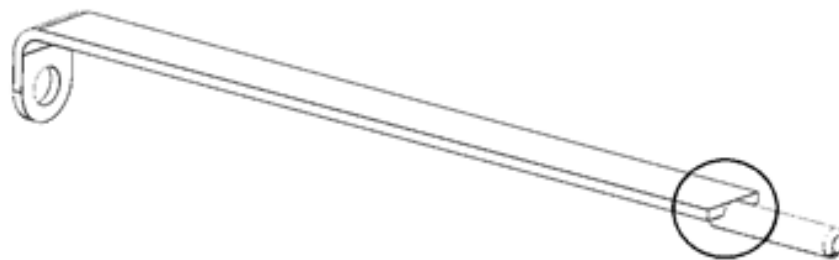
Конструктивне виконання елемента зварного з'єднання
